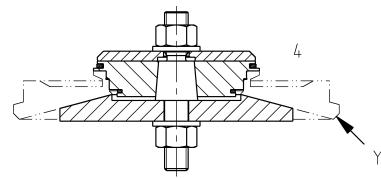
4=Schweißvorrichtung für Gehäuseanschluss T
